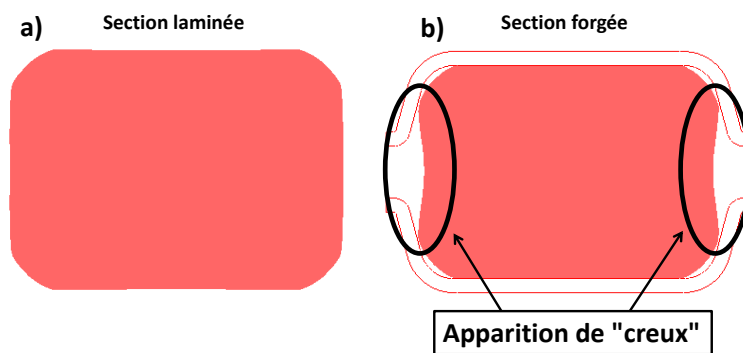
Aire a) de la barre après la cage 2 (31671mm^2) et b) du lopin après forgeage de la passe 2 (311mm^2)
